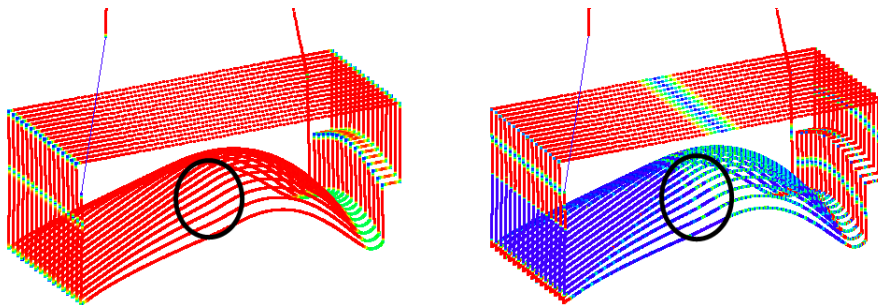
Links ist die reale Vorschubgeschwindigkeit einer Fräsmaschine beim Abfahren der Werkzeugbahnen zu sehen. Über die  $G^2$ -stetige Fläche hinweg bleibt der Vorschub maximal und konstant. Rechts ist die Beschleunigung des Bahnwegs abgebildet. Im Gegensatz zur ersten Variante ist hier im Falle des  $G^2$ -Patches mit Optimierung im Bereich des Übergangs weniger helle Stellen erkennbar. Das bedeutet, dass die Beschleunigung konstant bei fast  $0 \frac{mm}{s^2}$  (= blau) lag.
